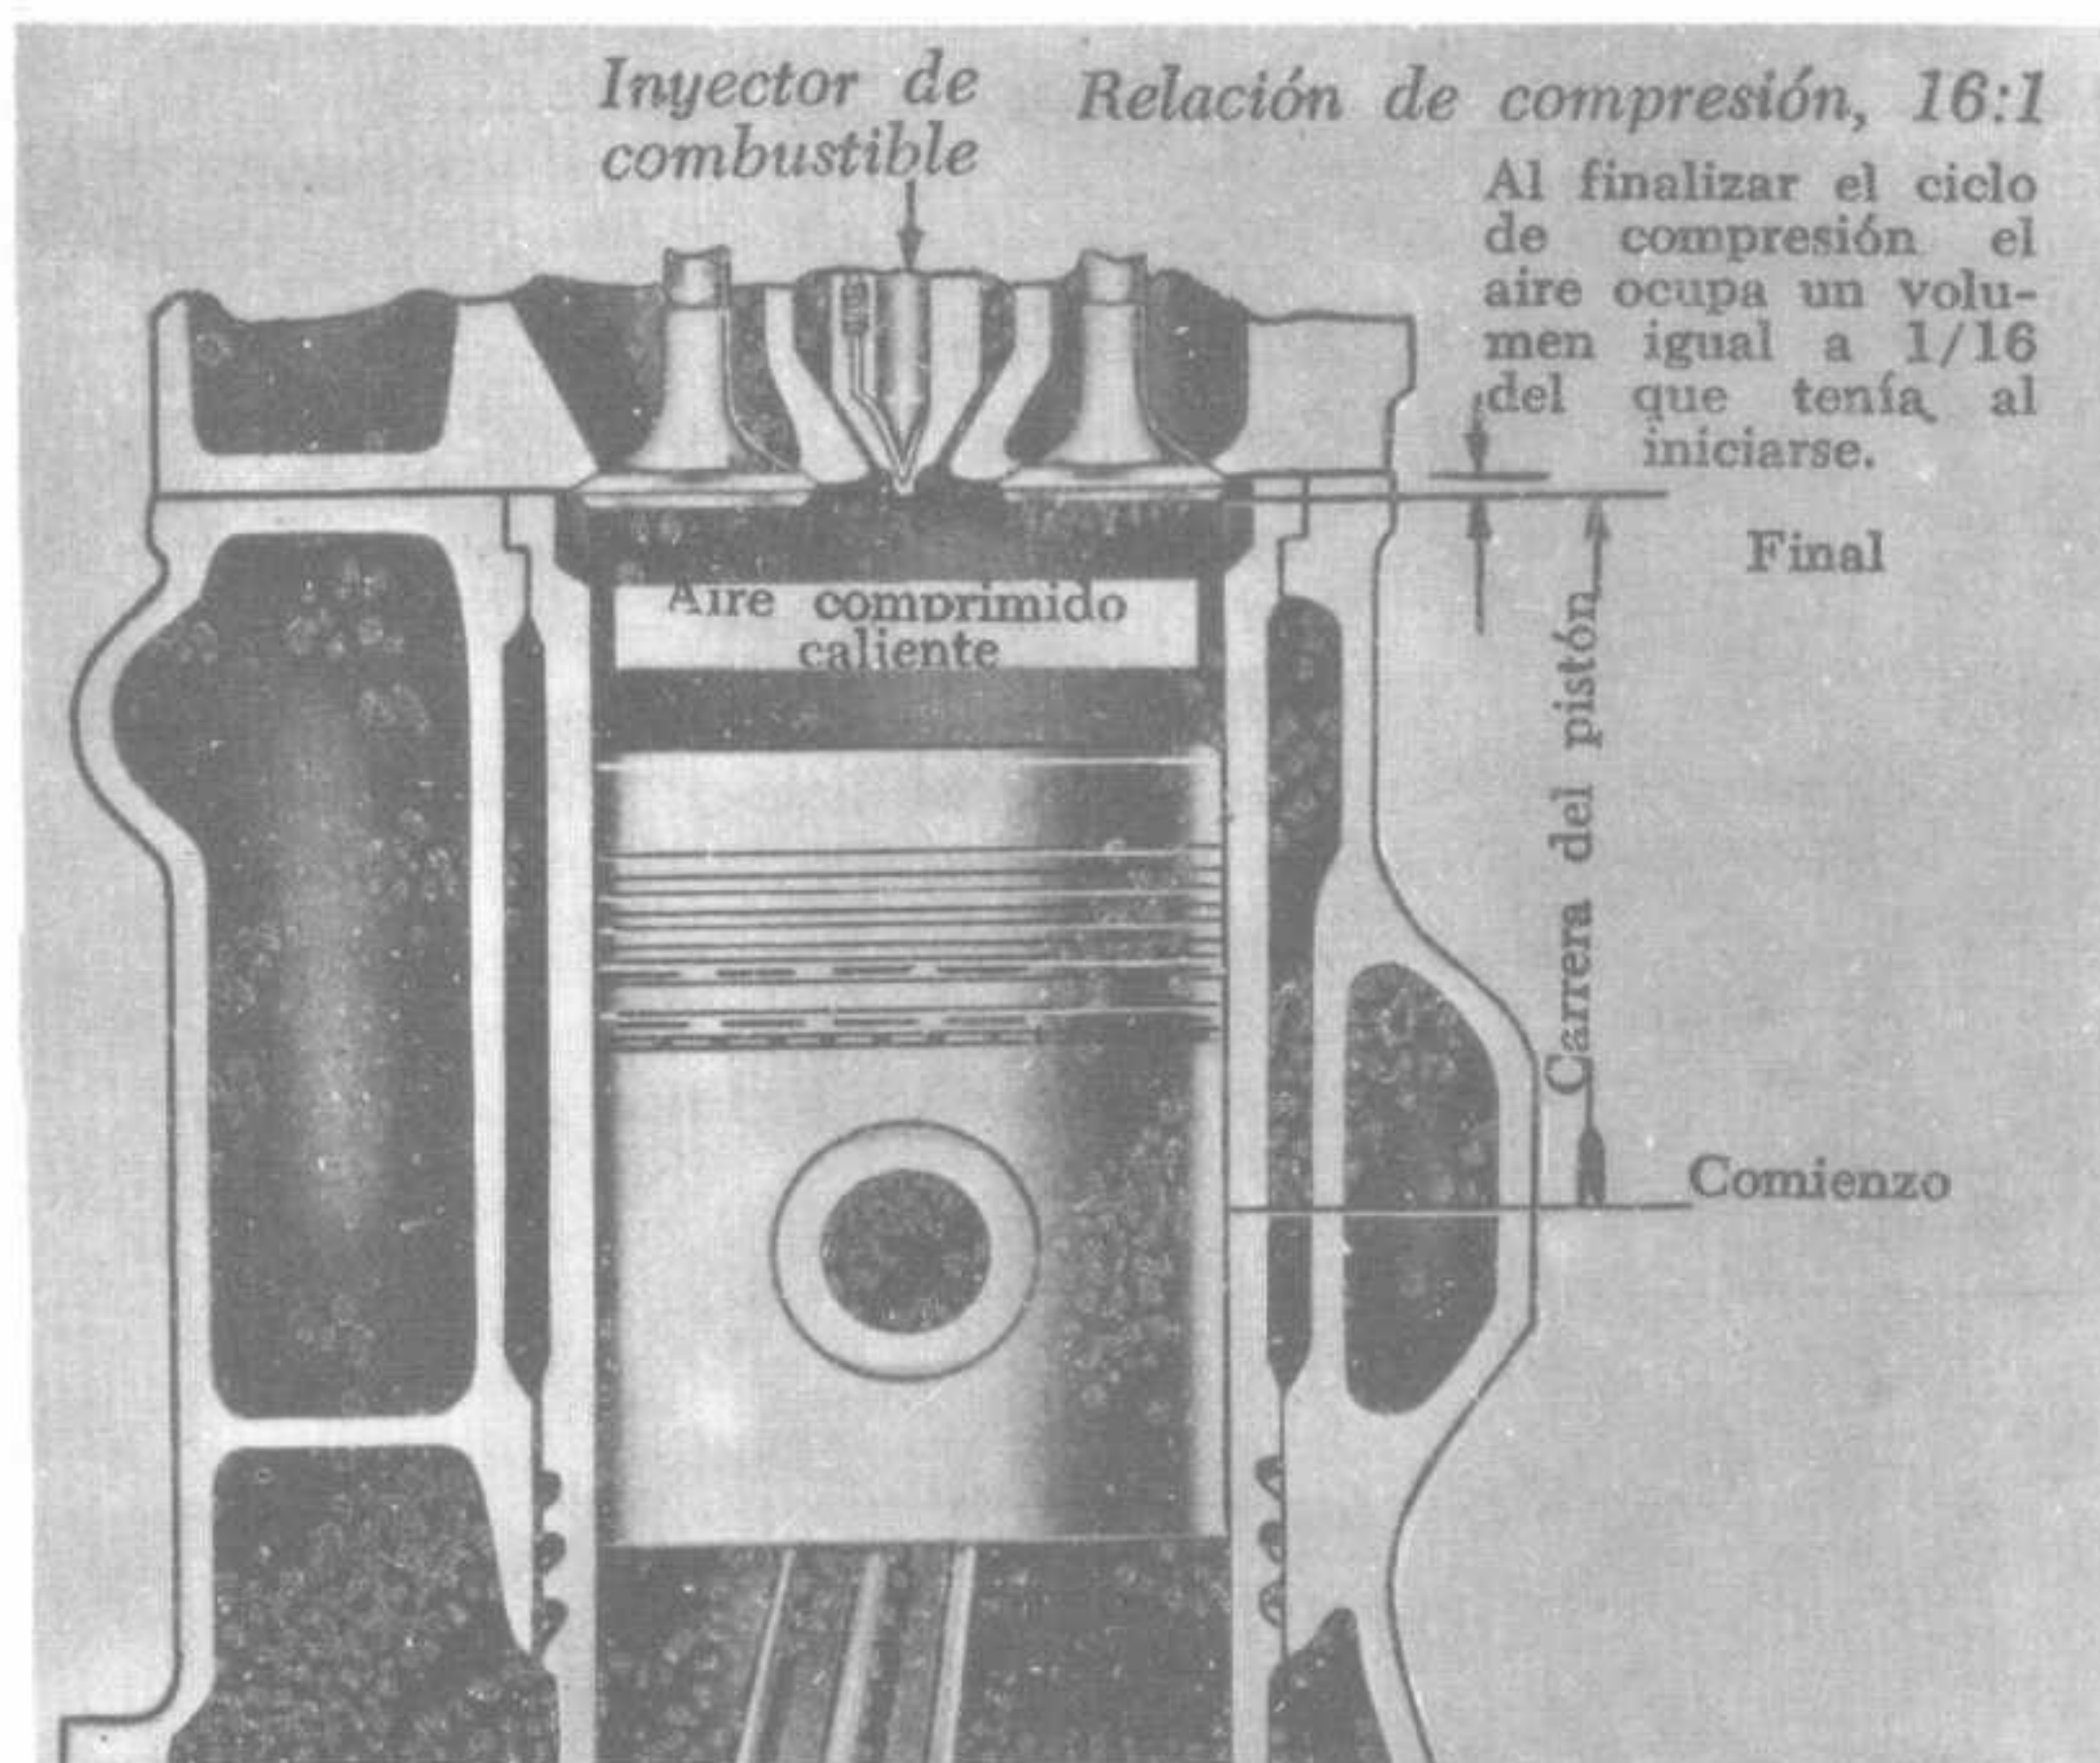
Corte del cilindro de un motor Diesel (tiempo de compresión).
